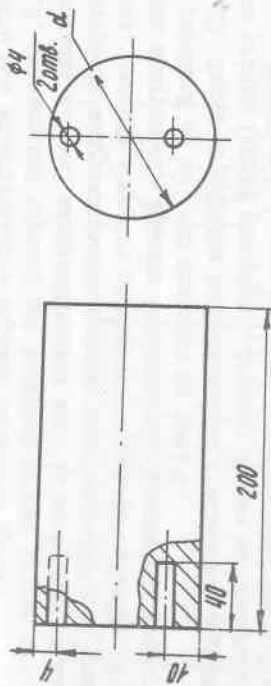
Стандартный образец для настройки ультразвукового прибора при контроле отвода:
